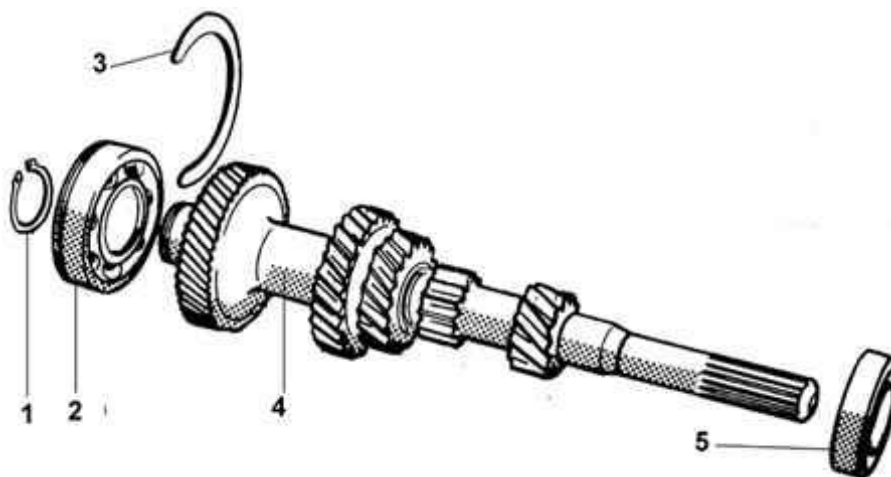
Первинний вал коробки перемикання передач: 1 – стопорне кільце; 2, 5 – підшипник; 3 – стопорне кільце підшипника; 4 – первинний вал
